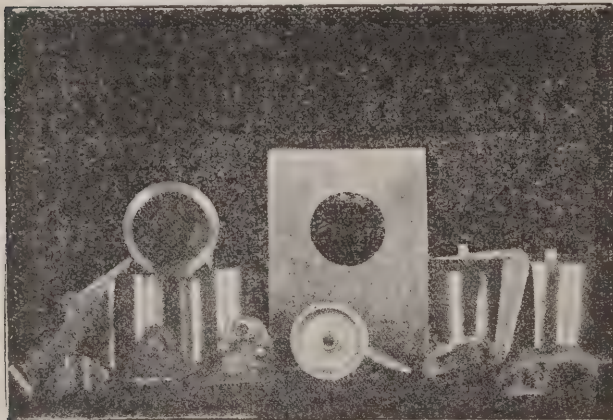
Pièces en magnésium moulé: pistons, carter, pièces d'avion.
